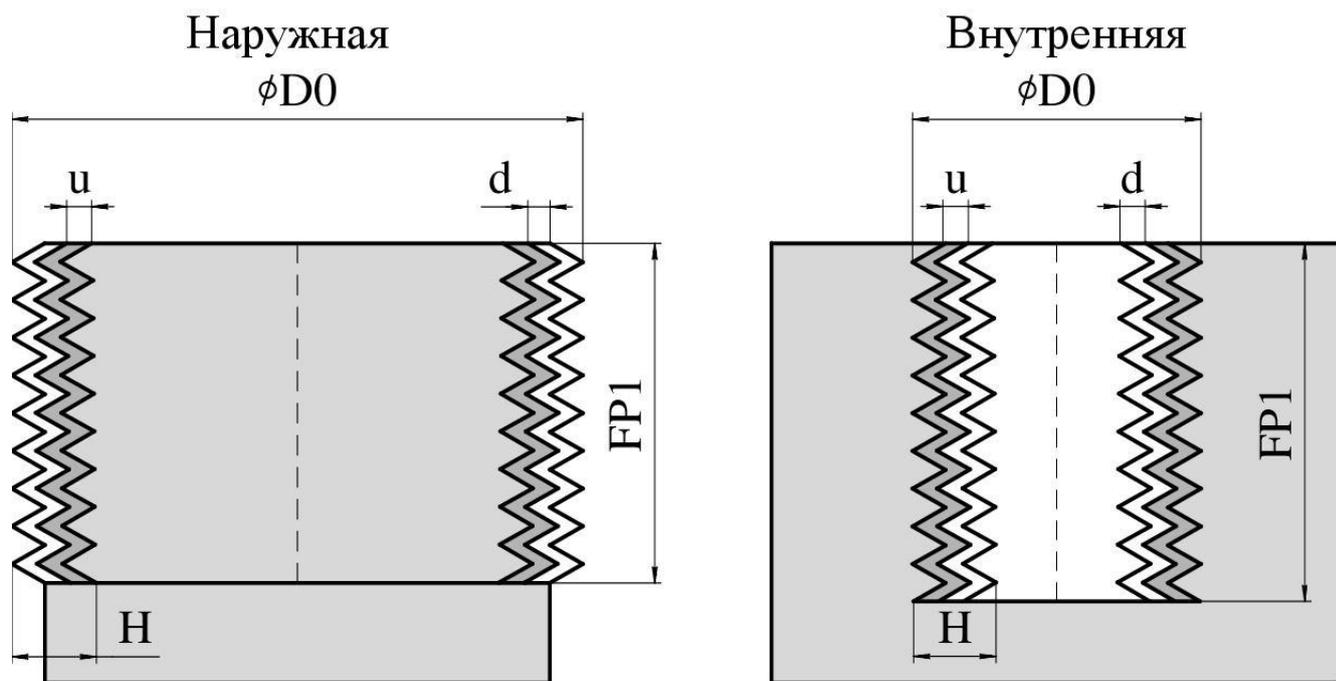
Переменные цикла фрезерования резьбы
